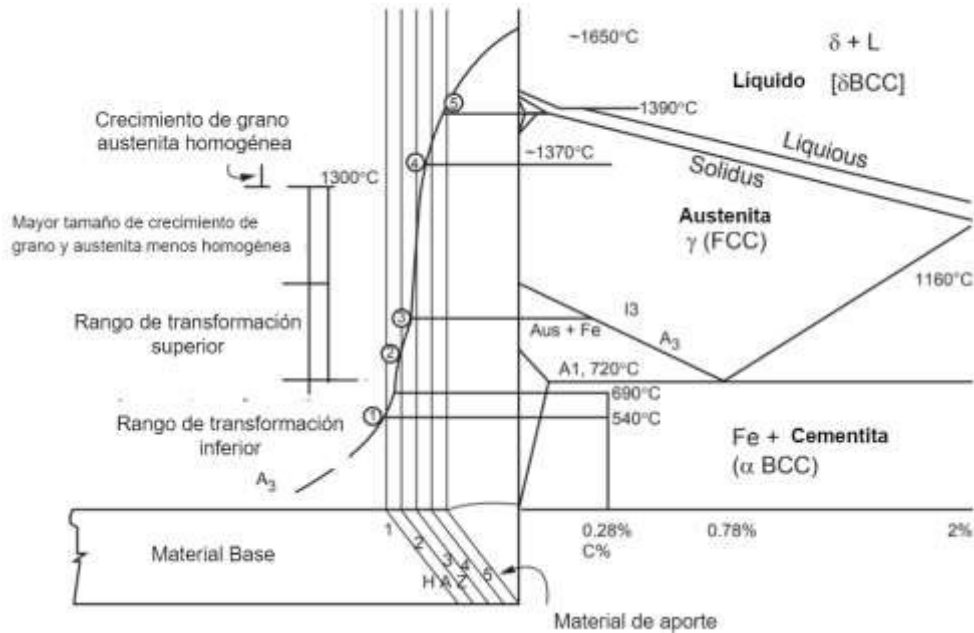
Efecto del calor en una soldadura, sobrepuesto sobre el diagrama de fases hierro carbono.
